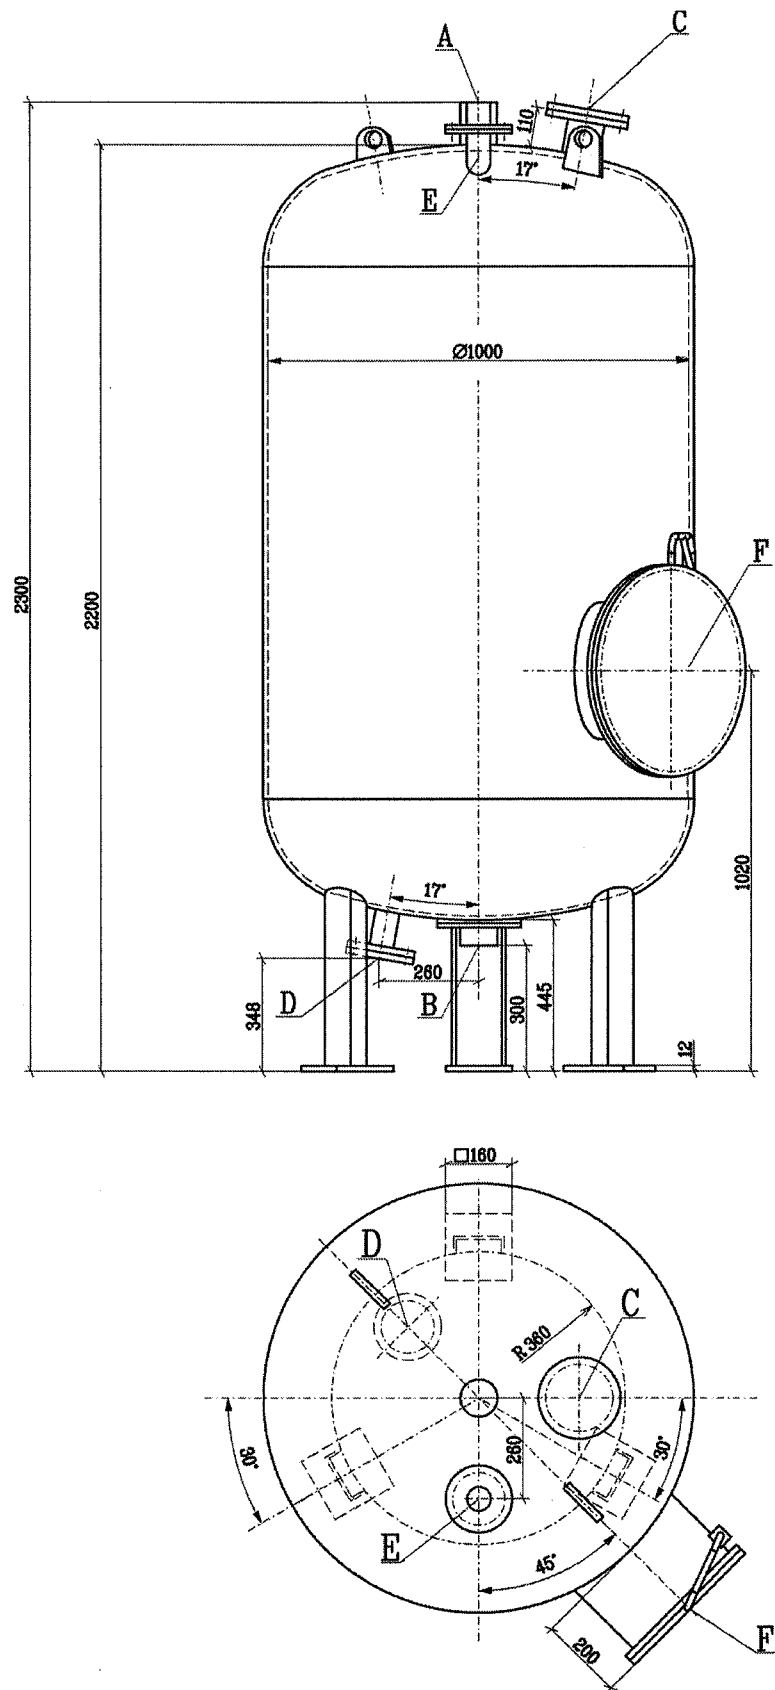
Габаритный чертеж фильтра фосфата QST10AT001
